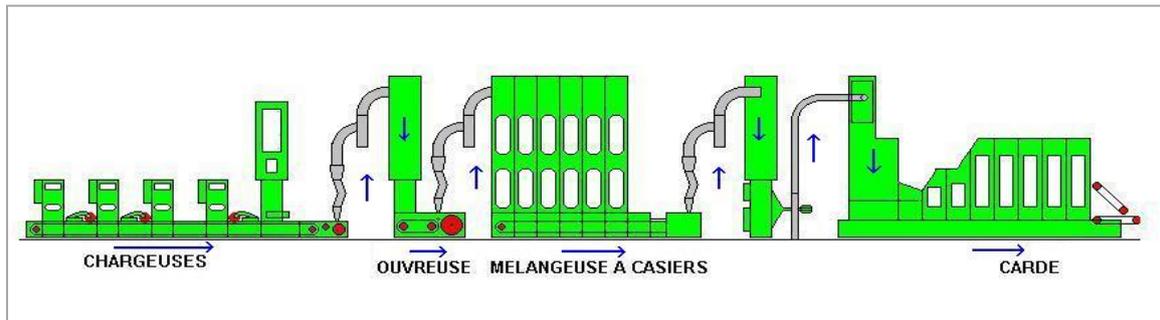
Schéma explicatif secteur thermo-soudé
